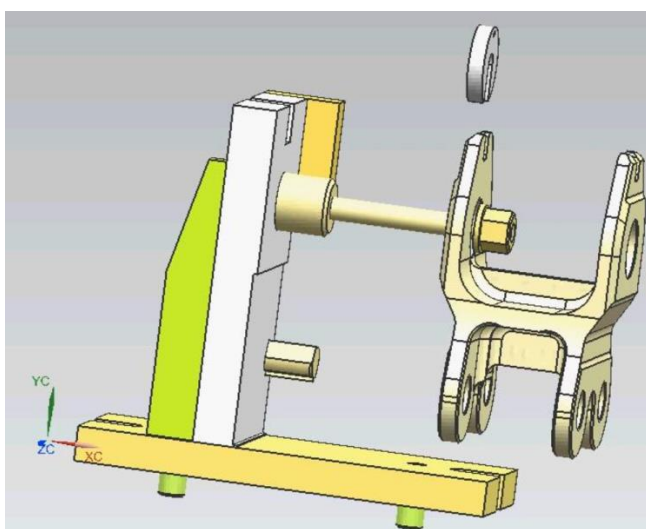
Момент движения закрепления-раскрепления заготовки.
